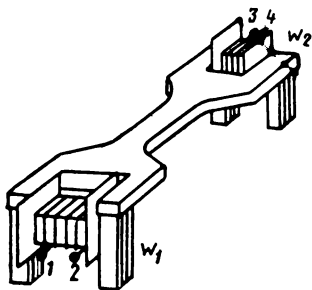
Приспособление для проверки правильности шага обмотки якоря:
